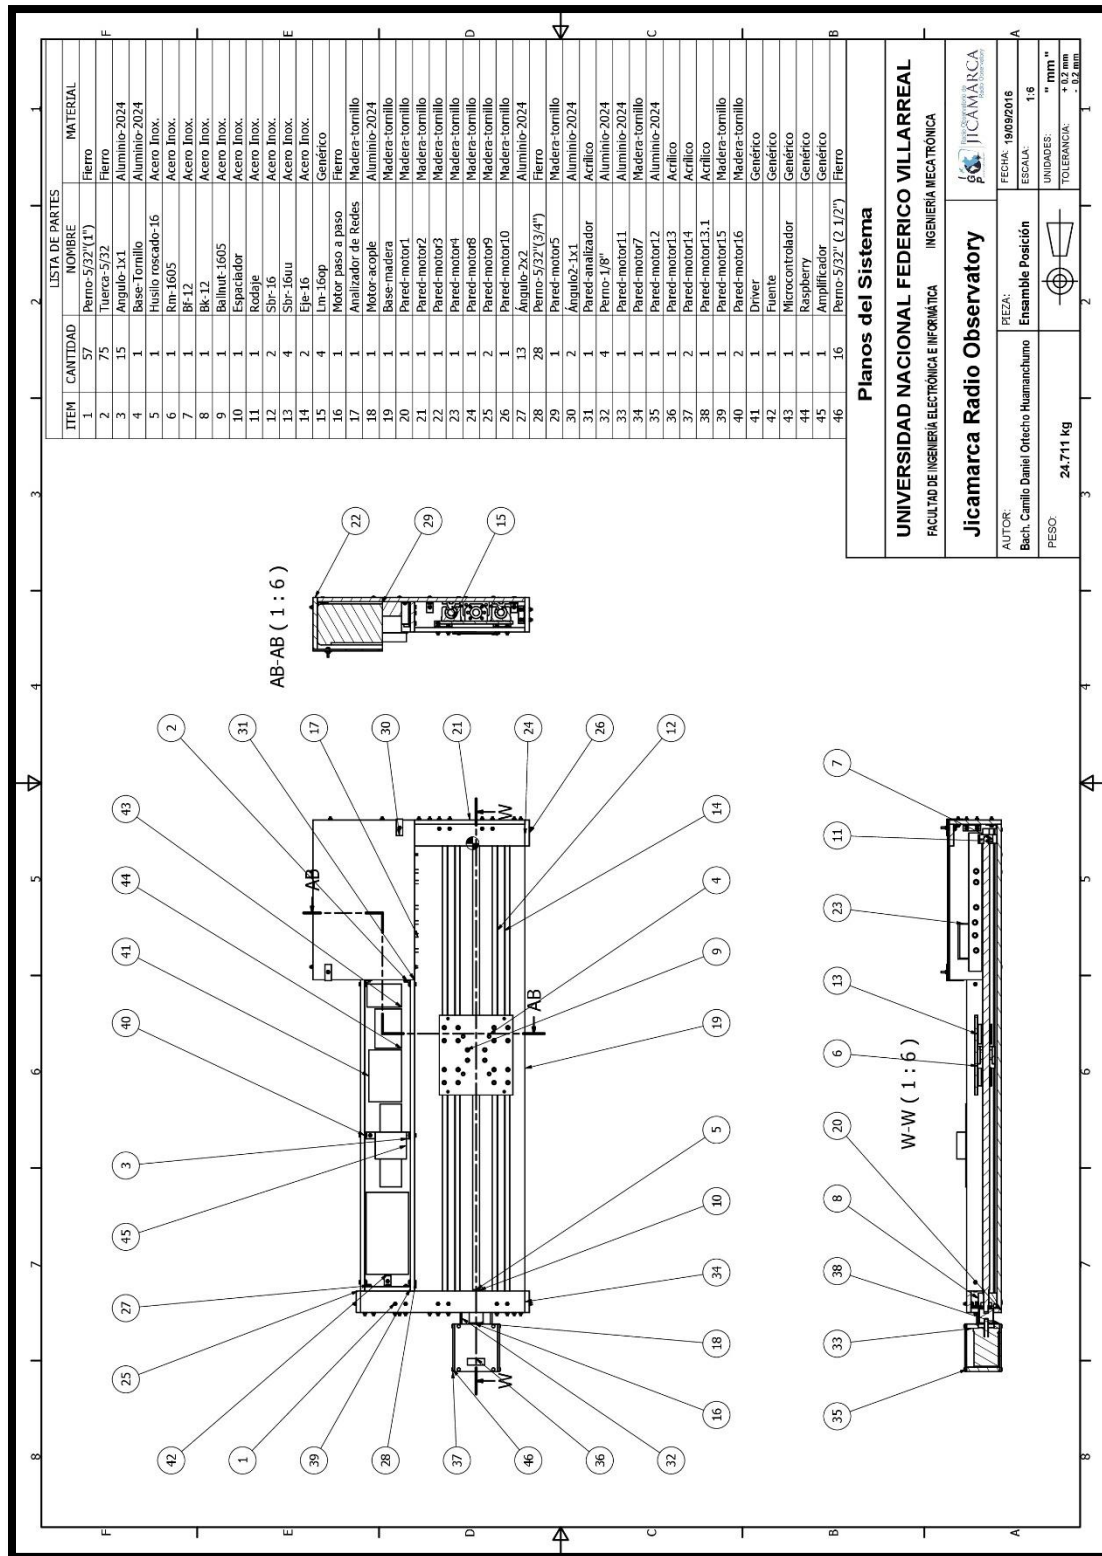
Plano del mecanismo de posición lineal (Fuente: el autor)
